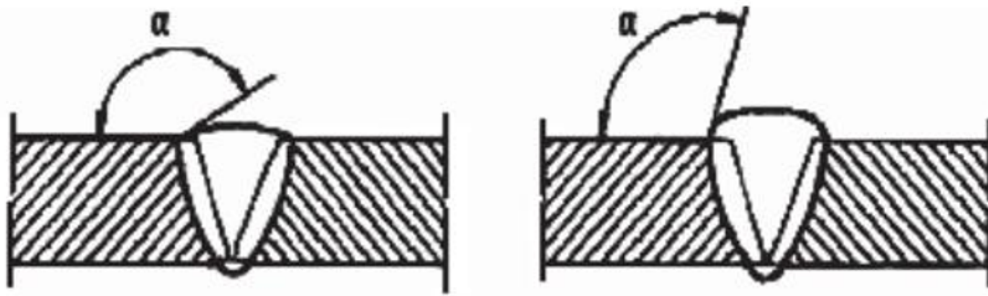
Эскиз дефекта сварного шва
